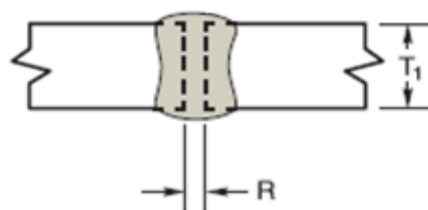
Sección de la soldadura típica de un tubo (Fuente: Wikipedia)
